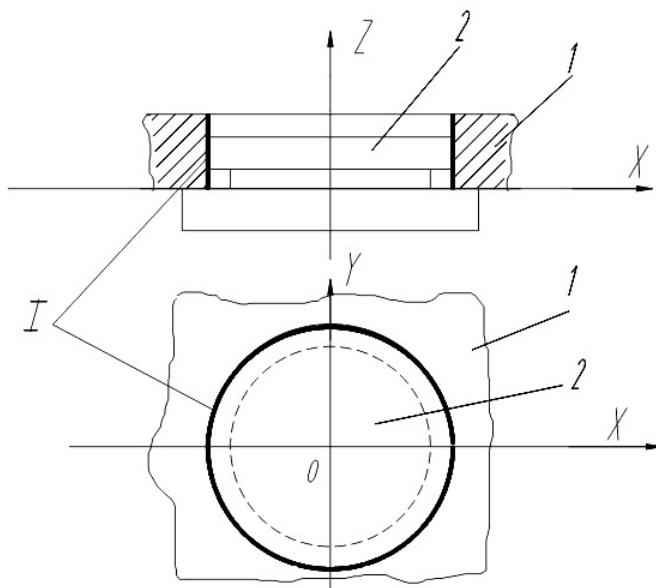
Двойная опорная база I, лишаящая перемещений заготовки вдоль осей  $OX$  и  $OY$ : 1 – заготовка; 2 – элемент приспособления
